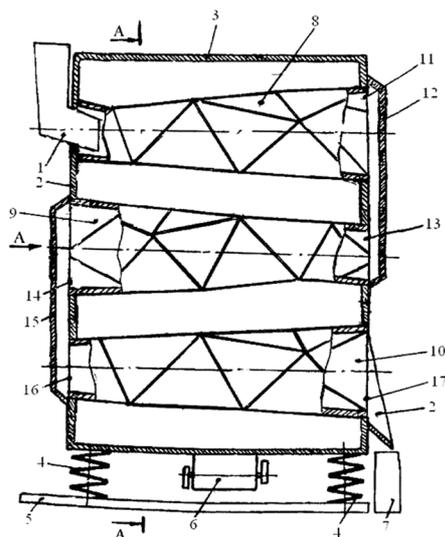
Малогабаритная установка для приготовления концентрированных кормов
